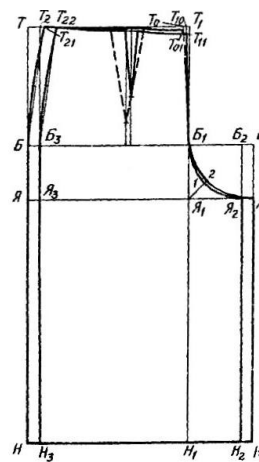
Чертеж конструкции юбки-брюк
